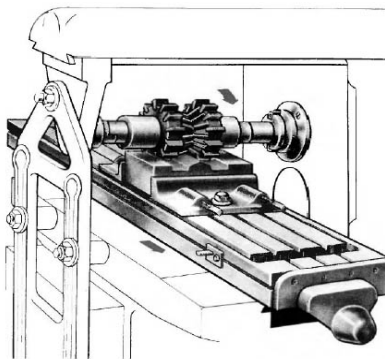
Обробка заготовки на горизонтально-фрезерному верстаті
